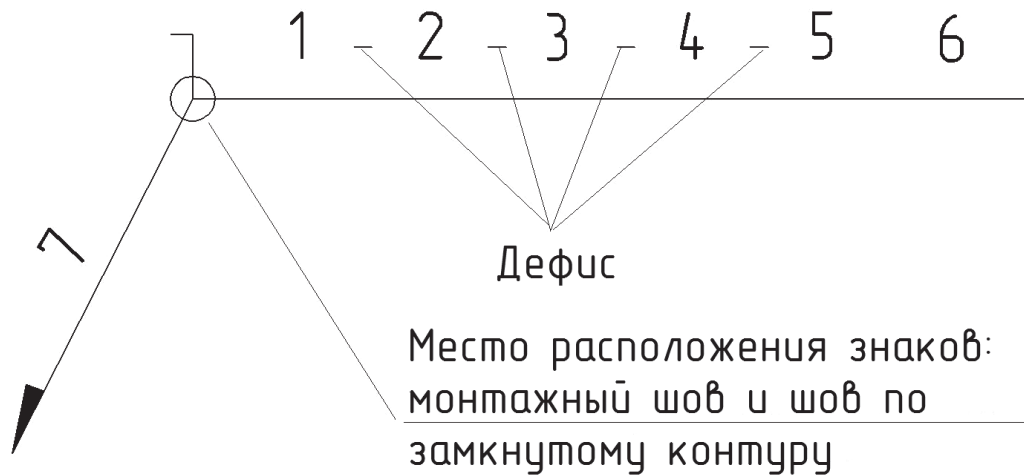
Структура условного обозначения стандартного сварного шва
